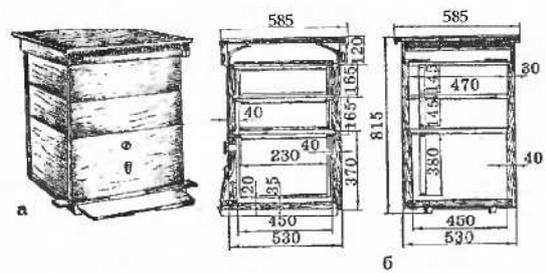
Двухкорпусный улей (размеры в мм): а — общий вид; б — устройство улья
